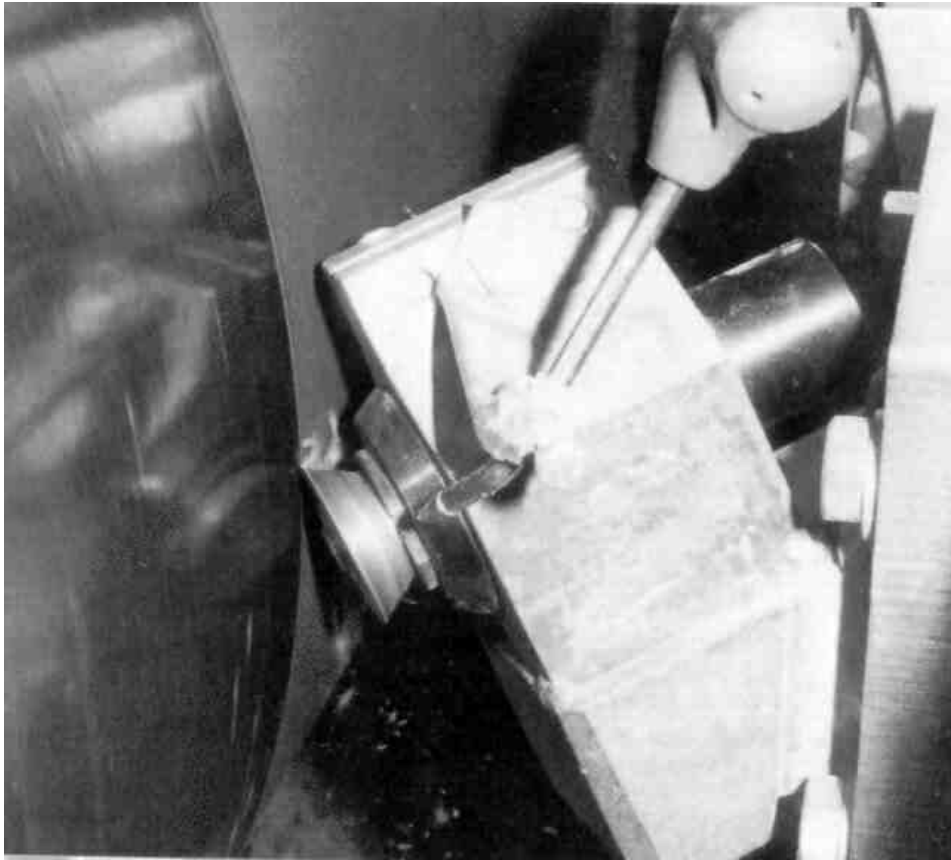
Обточка вала суперкаландра ротационным резцом с охлаждением режущей чашки воздухом
